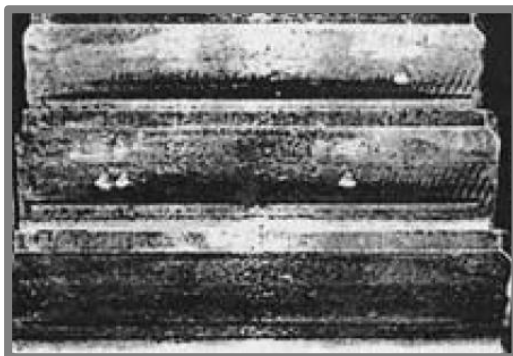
Abrazivní opotřebení pístu spalovacího motoru [15]
